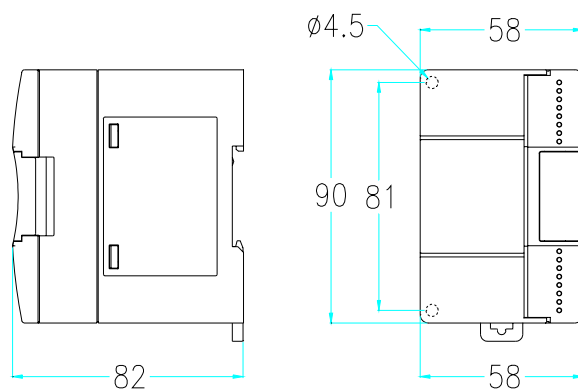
EC20 - 0808ER 及模拟量扩展模块外形尺寸与安装孔位尺寸
